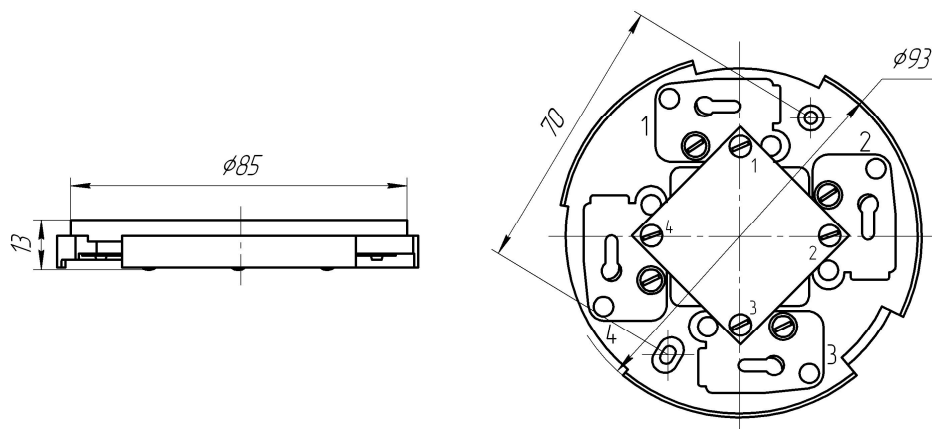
Внешний вид, габаритно-установочные размеры МКЗС, размеры в мм.
